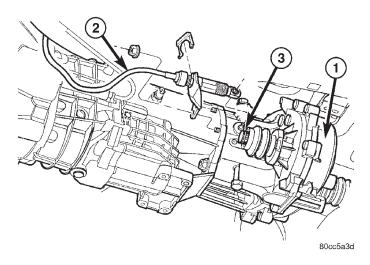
Cable de cambios de la caja de cambios -Transmisión manual
